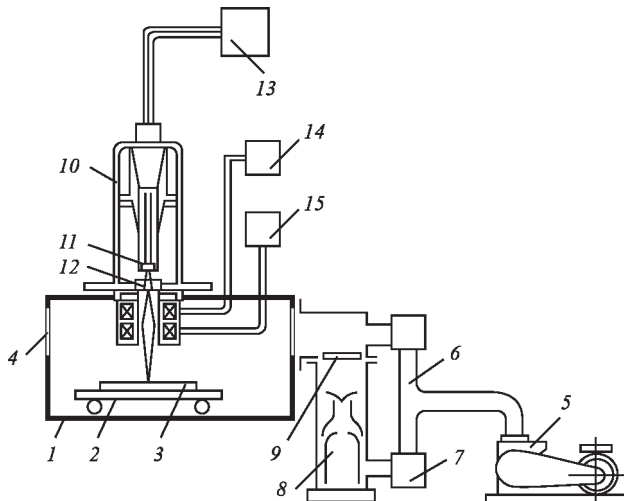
Схема електронно-променевої зварювальної установки: 1 — вакуумна камера; 2 — механізм переміщення; 3 — виріб; 4 — оглядове вікно; 5 — форвакуумний насос; 6 — вакуумпровід; 7 — вентиль; 8 — високовакуумний насос; 9 — затвор високовакуумного агрегата; 10 — зварювальна гармата; 11 — катод; 12 — анод; 13 — високовольтне джерело живлення; 14 — система фокусування променя; 15 — система електромагнітного відхилення пучка електронів
